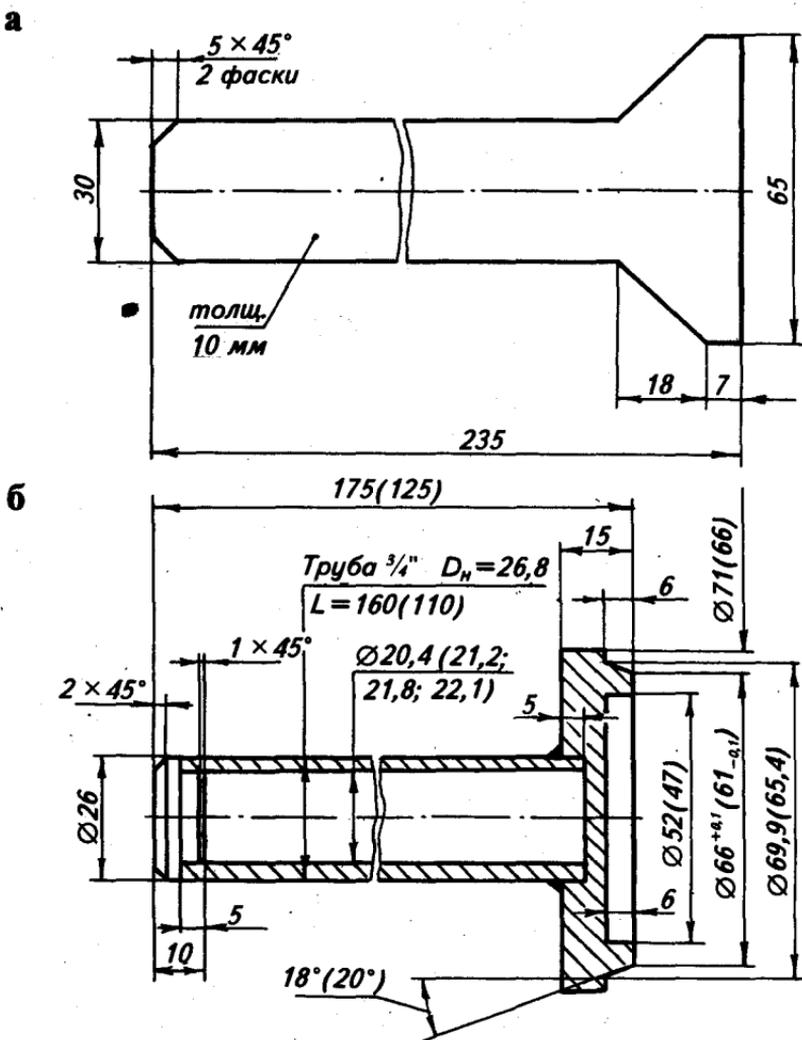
Подставка для разборки и сборки редуктора заднего моста:
